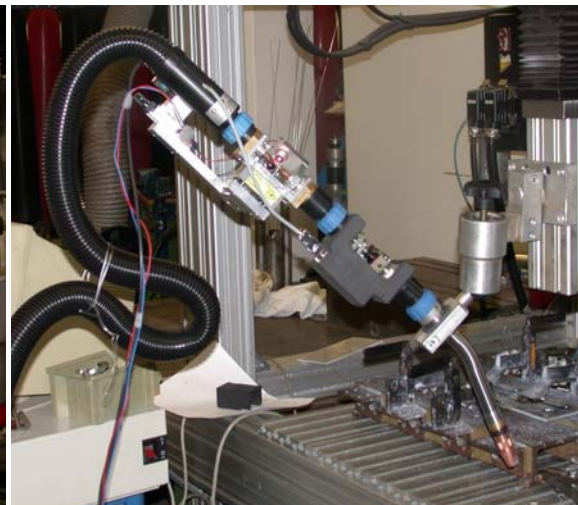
Anordnung des Schlauchpaketes mit erschwerten Drahtförderbedingungen
